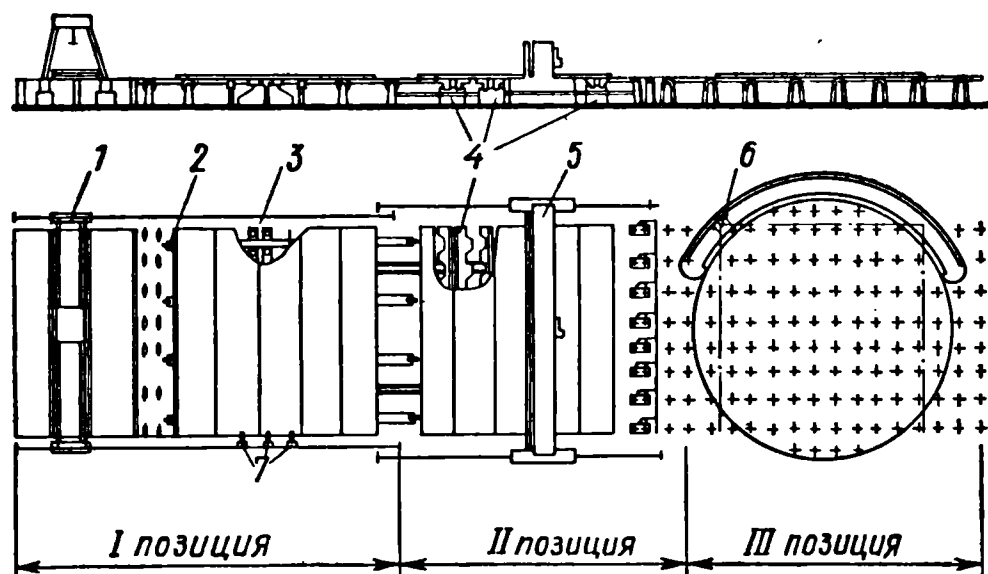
Схема поточной линии изготовления полотнищ с односторонней сваркой и обратным формированием шва на флюсомедной подкладке.
